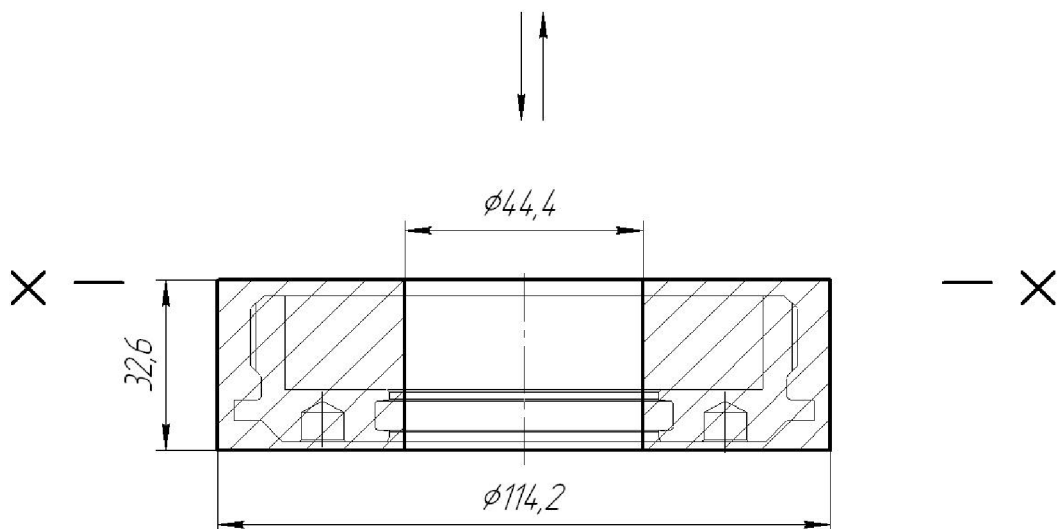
Ескіз заготовки, виготовленої на ГШП
